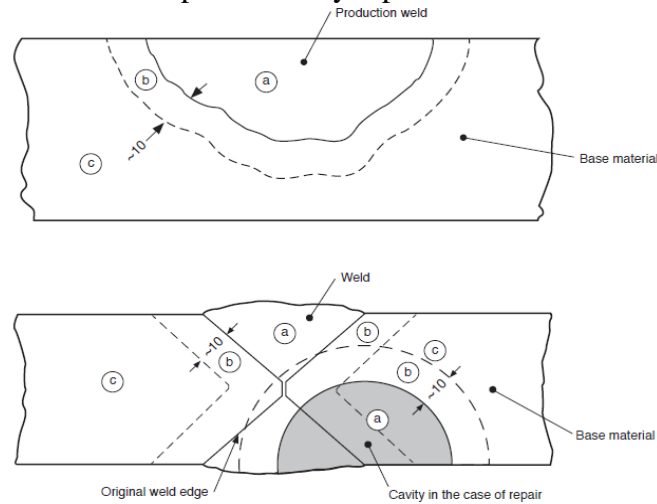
Soldadura de costura con penetración parcial y soldadura de costura con refuerzo
